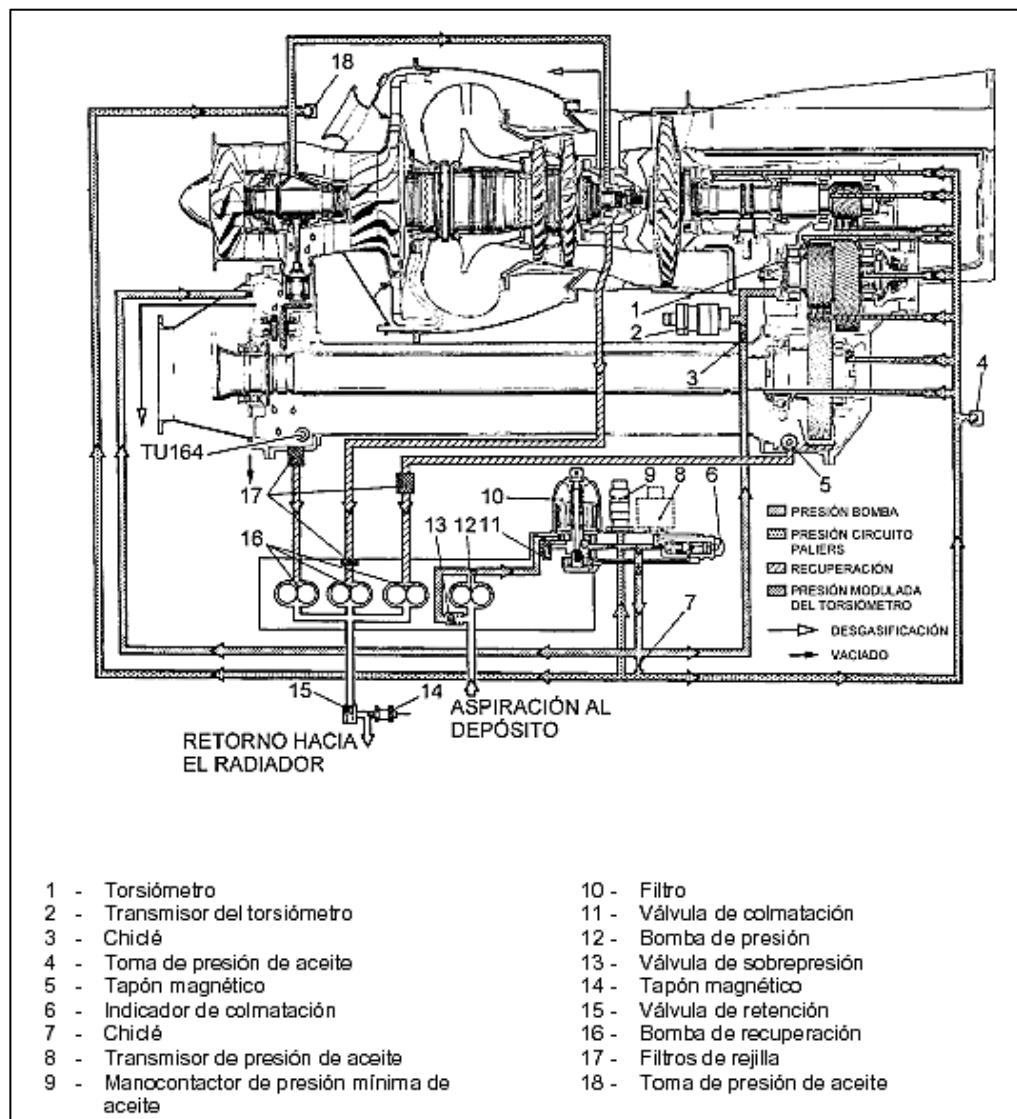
Partes del circuito de lubricación del motor ARRIEL 1B
